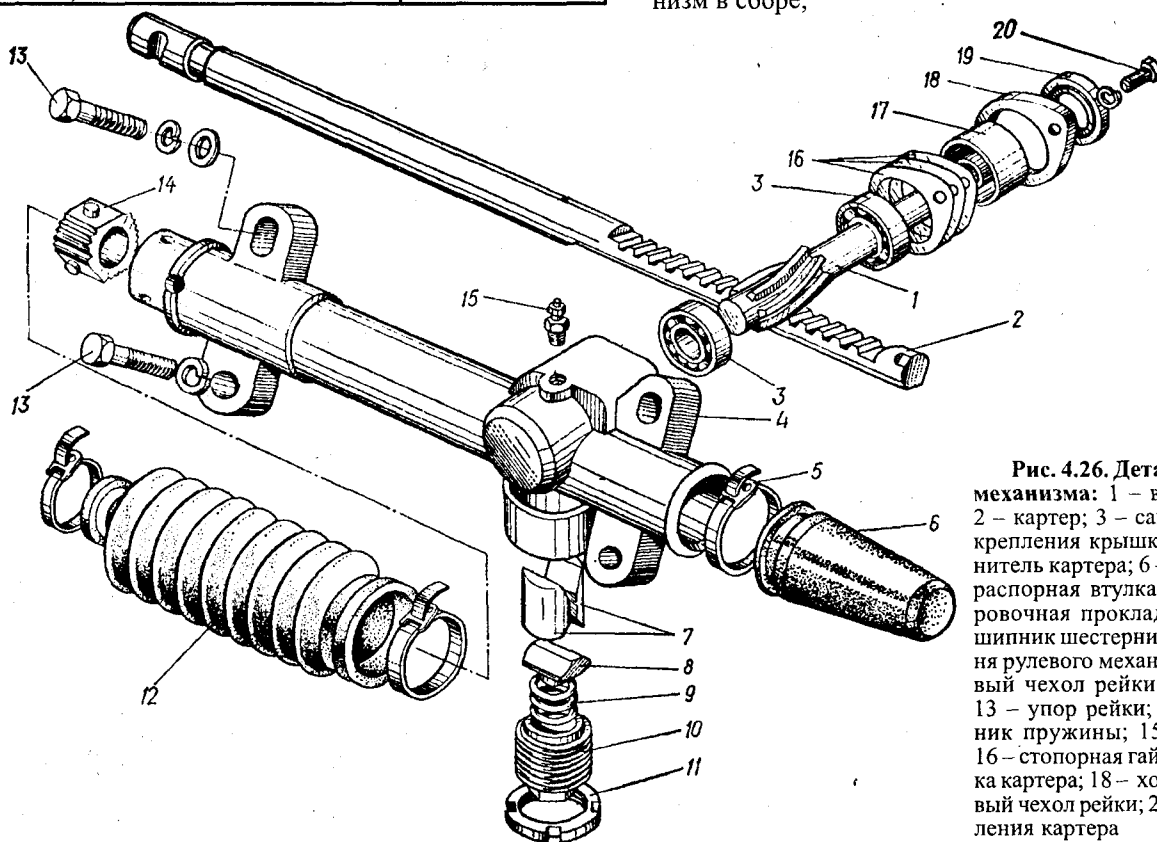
Детали рулевого механизма: 1 – втулка рейки; 2 – картер; 3 – сапун; 4 – болт крепления крышки; 5 – уплотнитель картера; 6 – крышка; 7 – распорная втулка; 8 – регулировочная прокладка; 9 – подшипник шестерни; 10 – шестерня рулевого механизма; 11 – левый чехол рейки; 12 – рейка; 13 – упор рейки; 14 – подпятник пружины; 15 – пружина; 16 – стопорная гайка; 17 – пробка картера; 18 – хомут; 19 – правый чехол рейки; 20 – болт крепления картера
